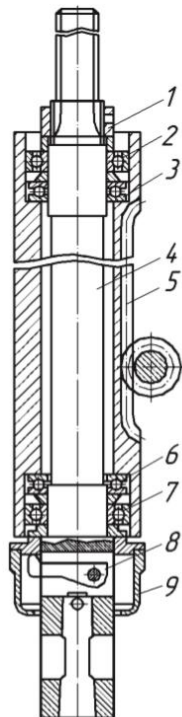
Привод подачі шпиндельного вузла шестерня-рейка. [9]
